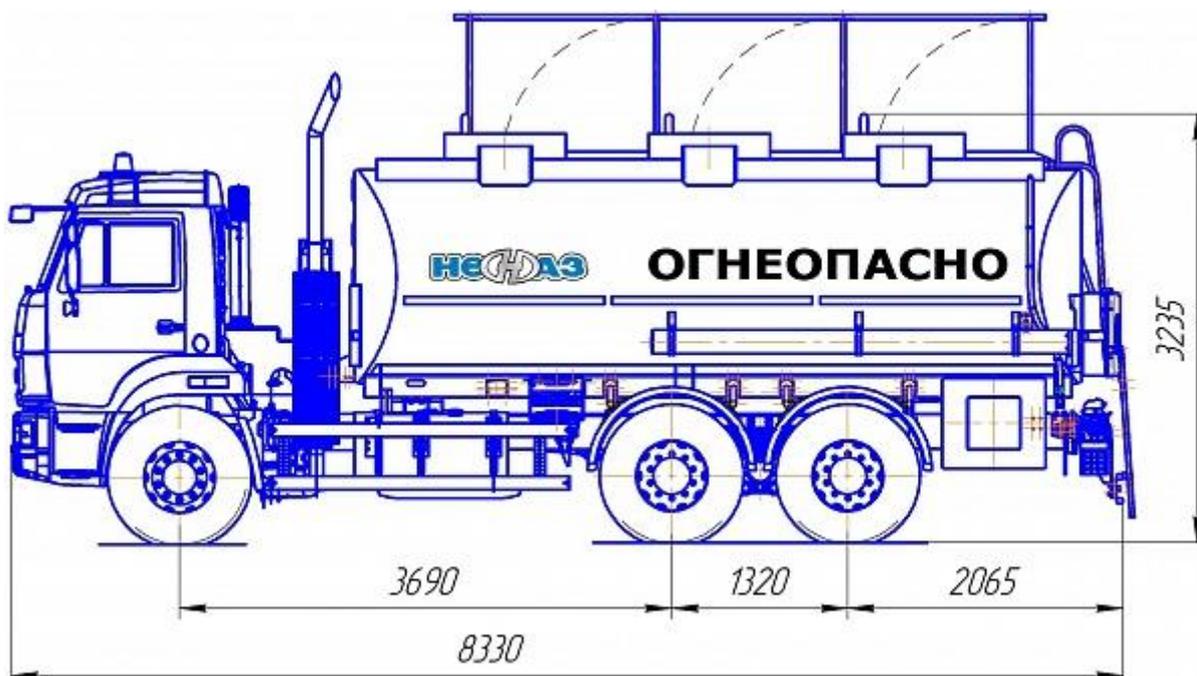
Габаритные размеры автотопливозаправщика АТЗ-20 на базе Камаз 66052
